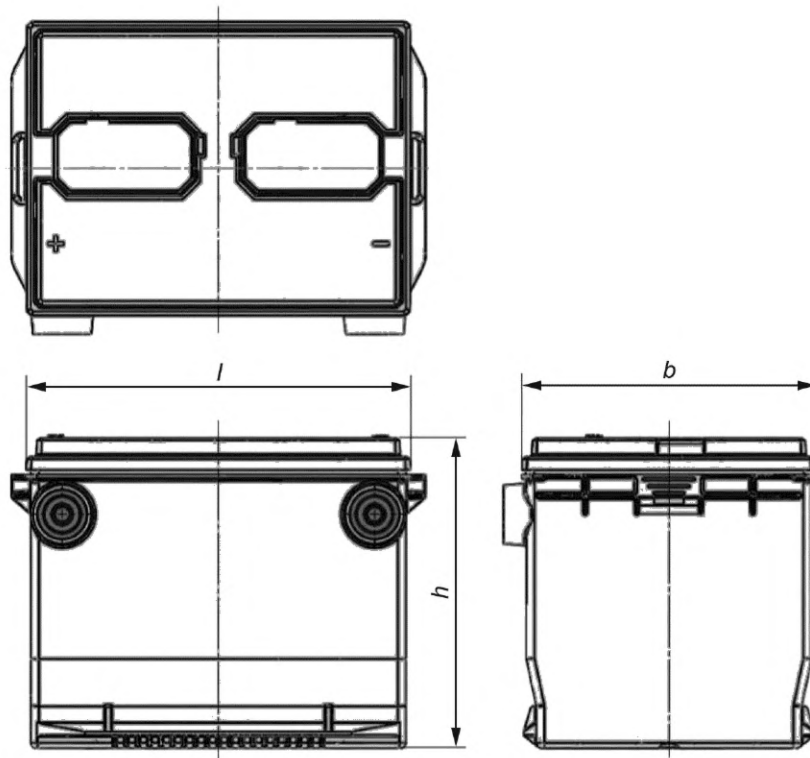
Основные размеры батарей типоразмеров 75, 78, 100 с боковым положительным выводом, расположенным на корпусе батареи слева
